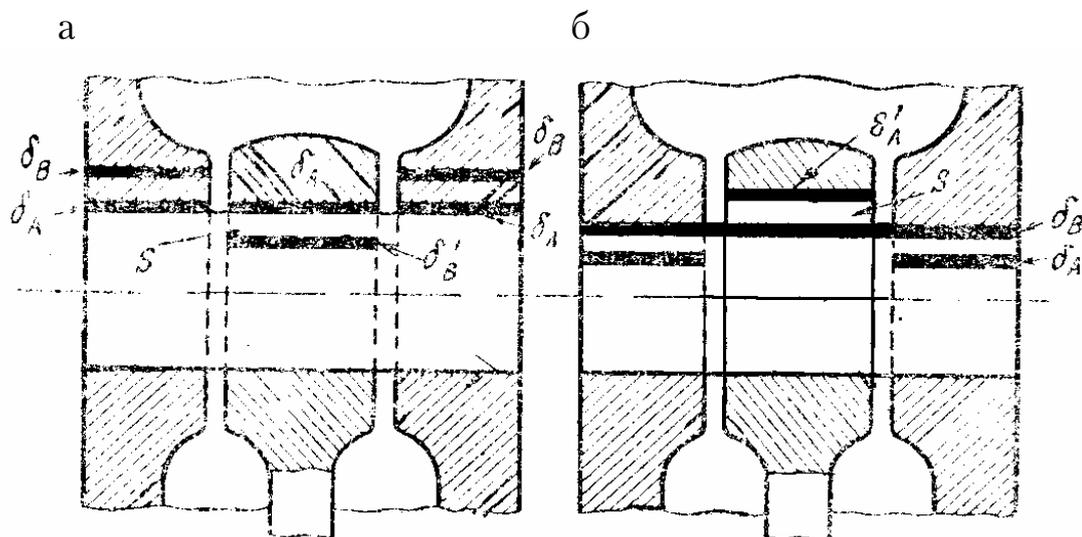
Положение полей допуска для сопряжения деталей в СО (а) и СВ (б)
